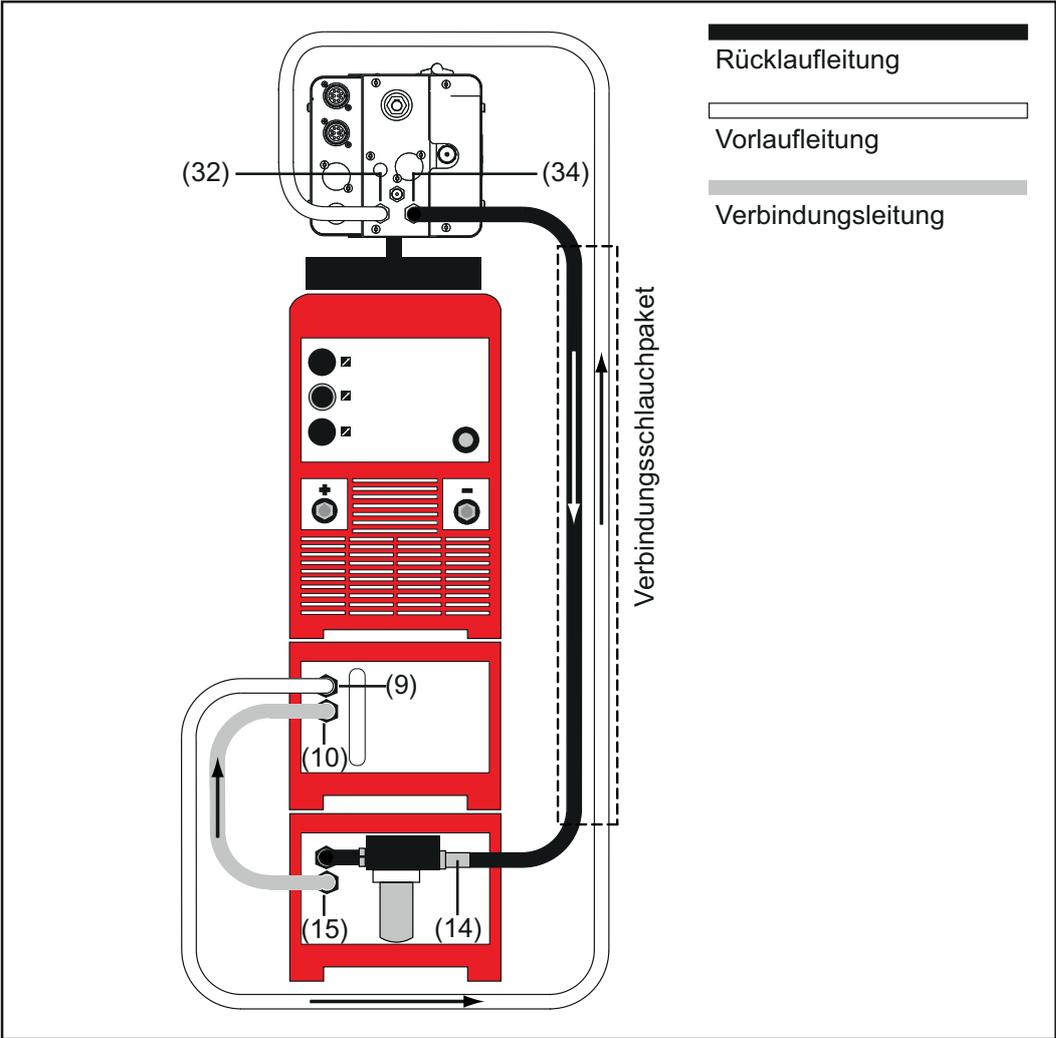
Kühlmittel-Anschlüsse bei TS / TPS 4000 / 5000 (Rückansicht)
